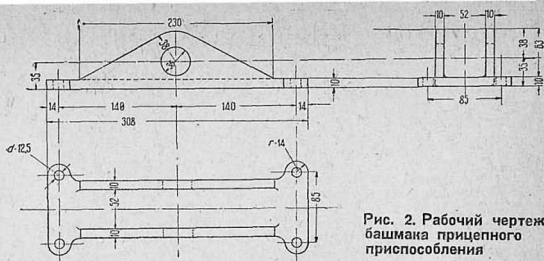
Рабочий чертеж башмака прицепного приспособления
